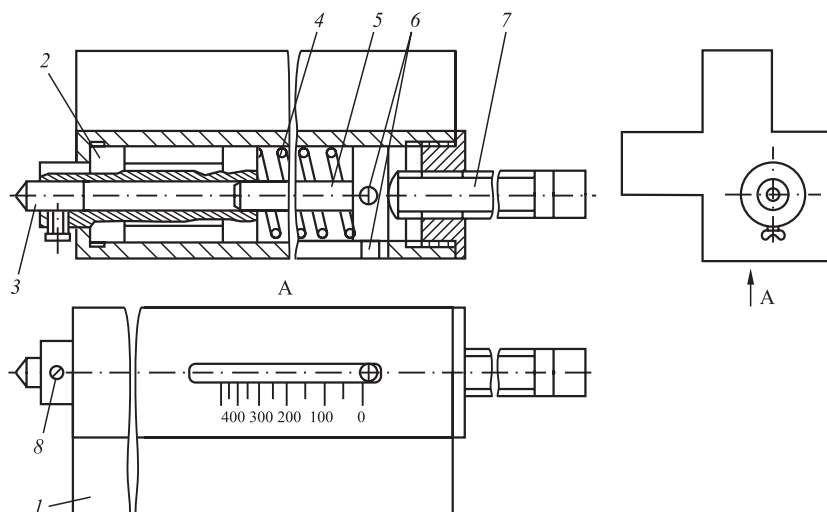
Устройство для выглаживания цилиндрических, конических и торцевых поверхностей на станках токарной группы
